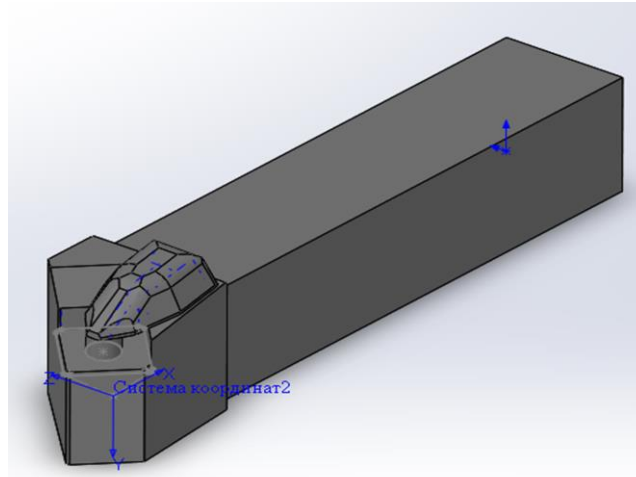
Модель токарного різця DSSNR 3232P 19
